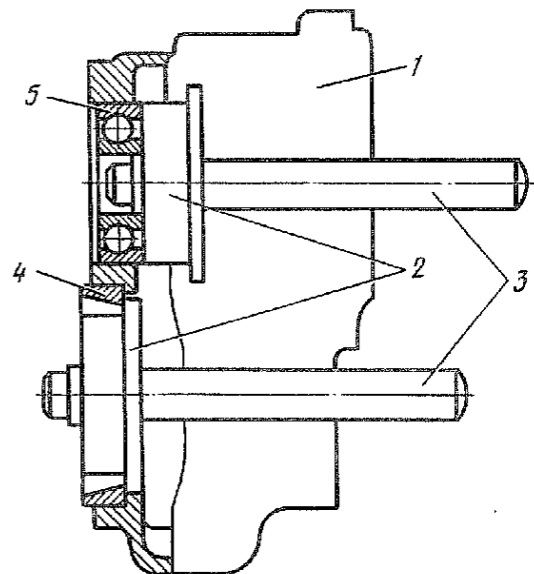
Выпрессовка наружных подшипников колесного редуктора:
